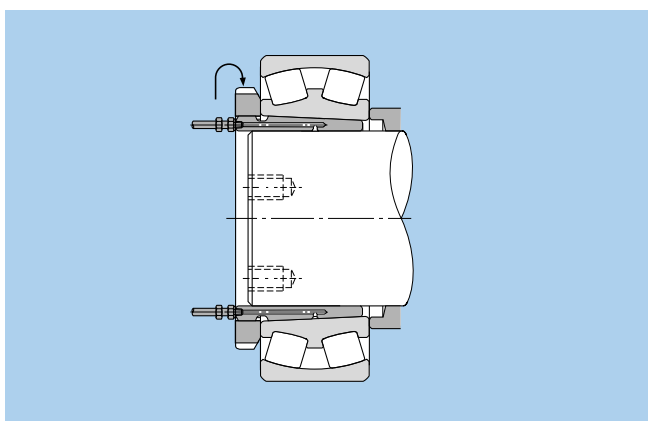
Remoción del rodamiento por presión hidráulica
